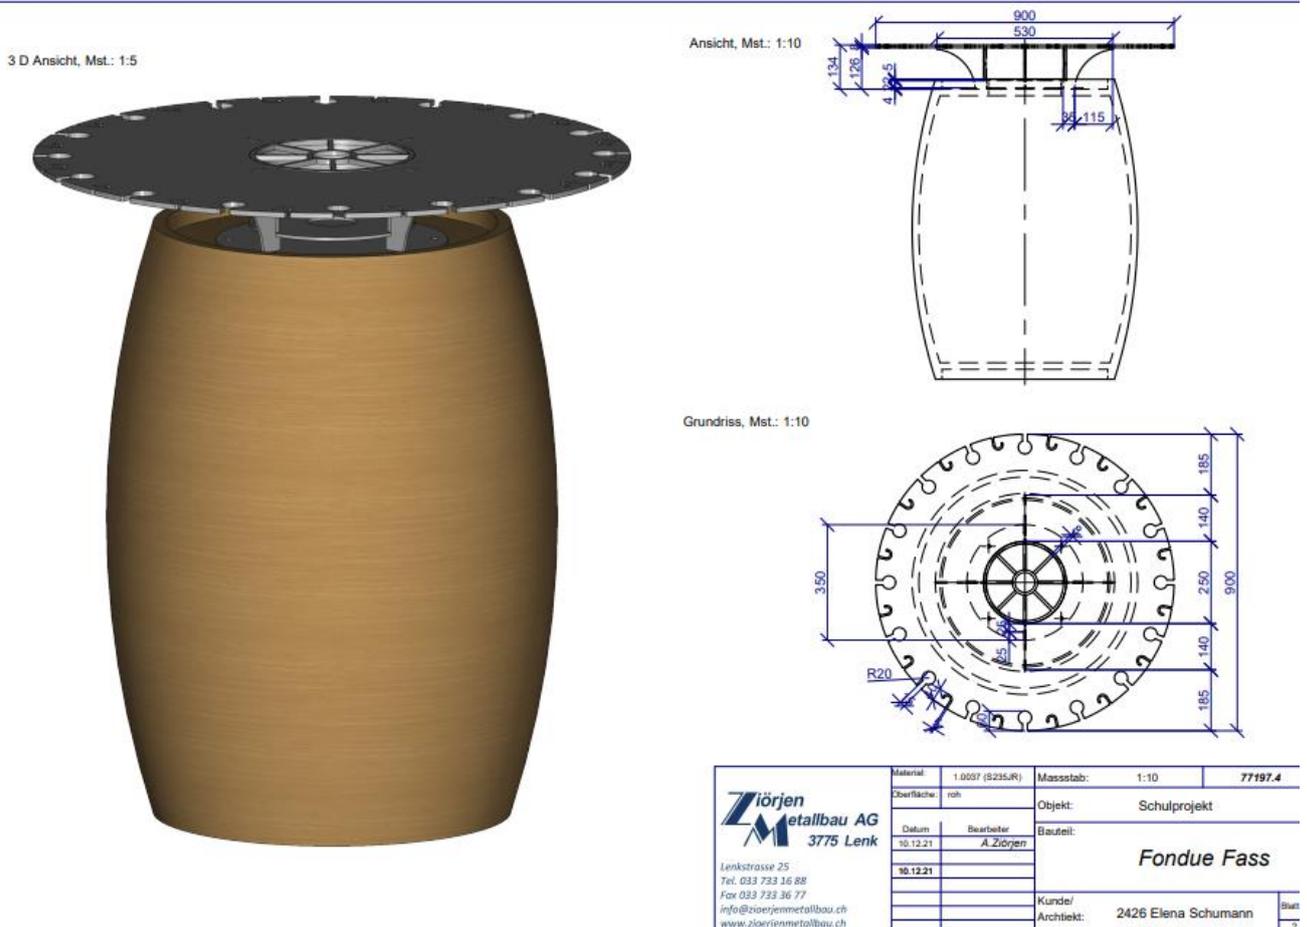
Plan Fonduefass, Elena Schumann, 15. Dezember 2021
